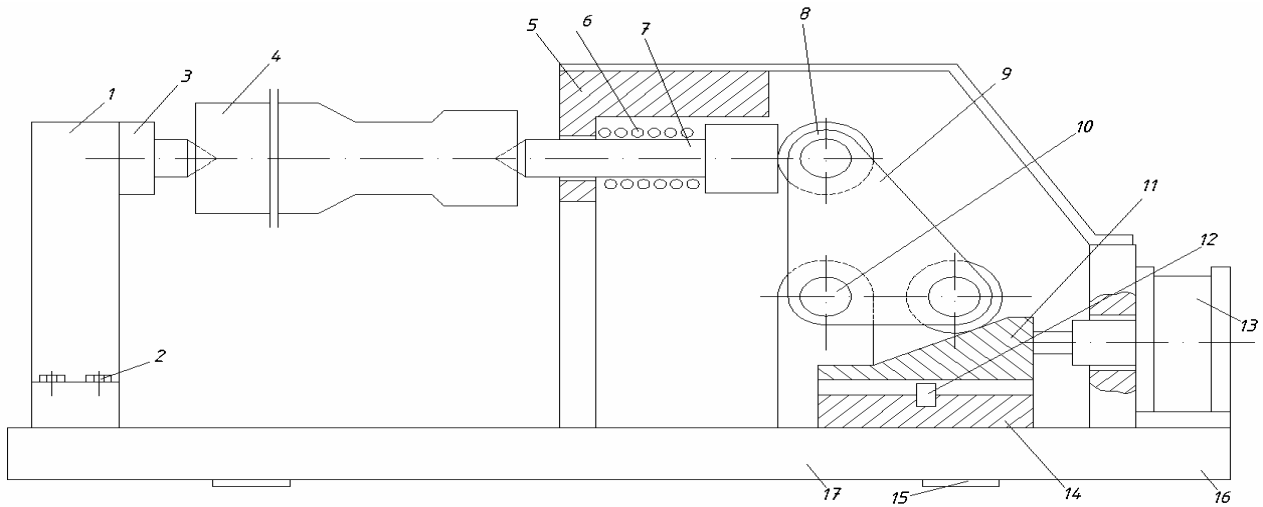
Приспосіблення для фрезерування двох пазів
